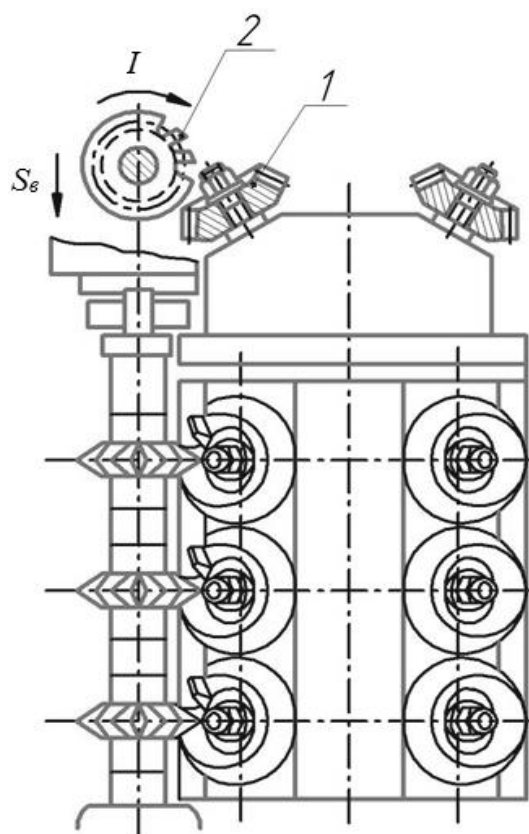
Чорнове нарізування зубів конічних коліс набором фрез
